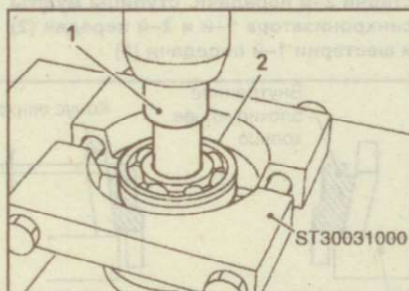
Использование прессы и оправки (1) для выпрессовки заднего подшипника (2) с вторичного вала
